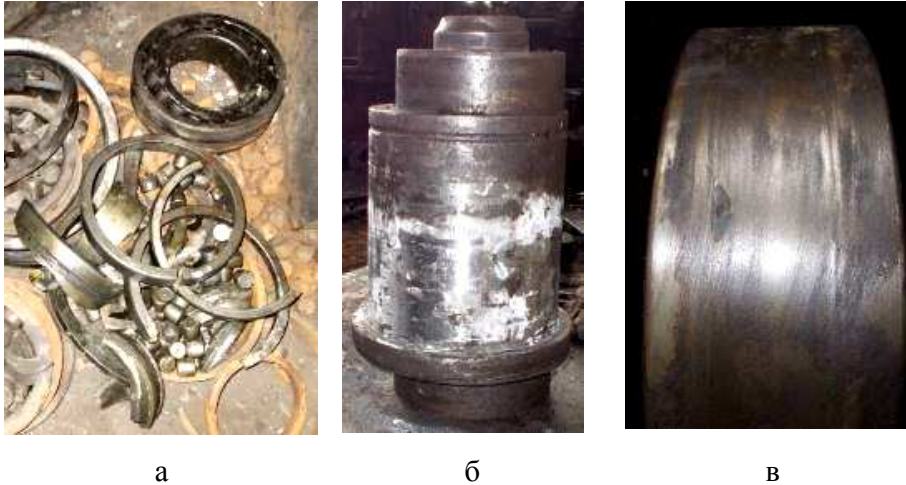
Поломки й uszkodження деталей касети кліті 580: зруйновані сферичні роликпідшипники (а); uszkodження поверхні осі (задирки) (б); задирка на робочій поверхні валка (в)
